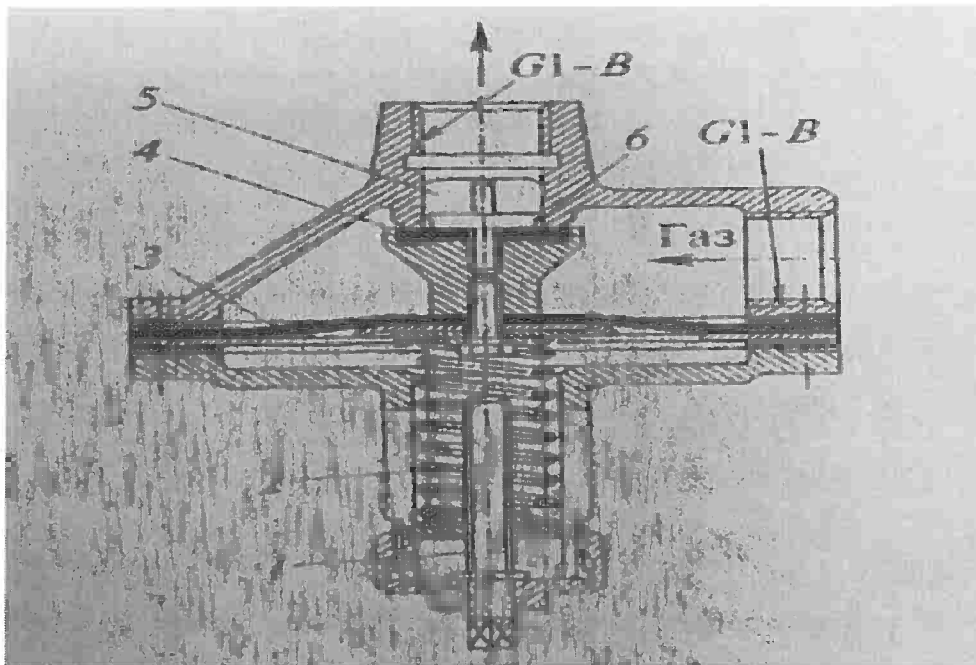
Предохранительно-сбросной клапан (ПСК): 1- регулировочный винт; 2-пружина; 3- мембрана; 4- уплотнение; 5- золотник; 6- седло.
